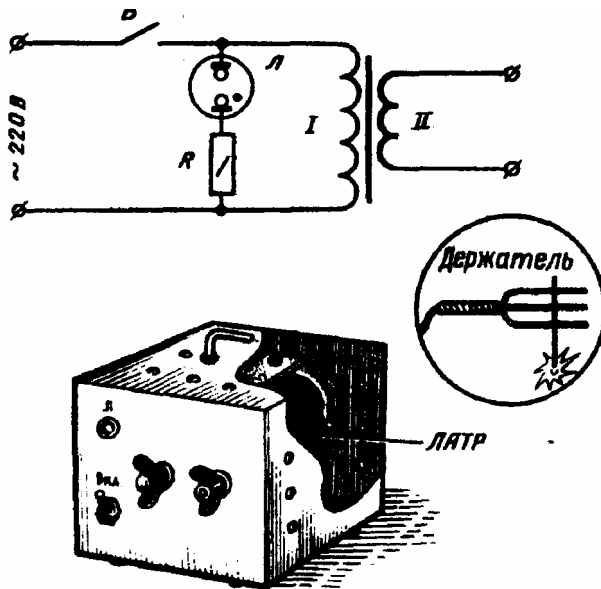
Портативный сварочный аппарат (первая конструкция).
